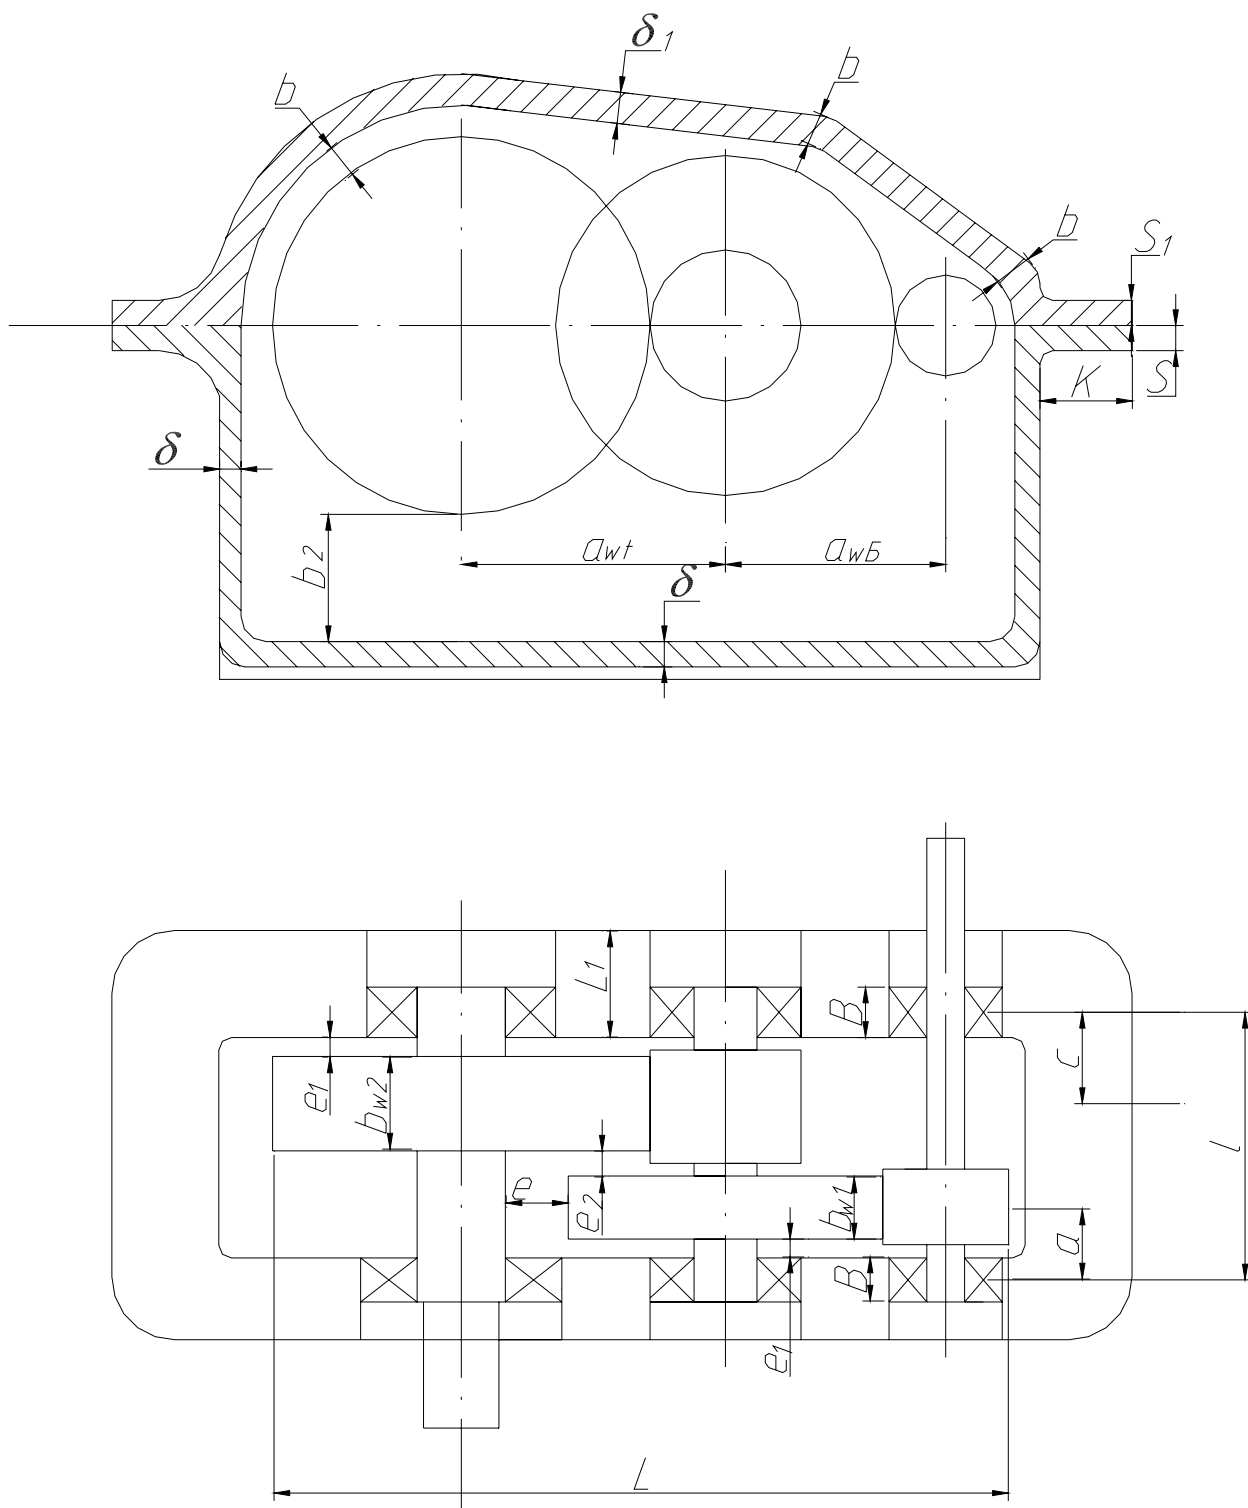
Компоновка двухступенчатого редуктора с развёрнутой схемой
